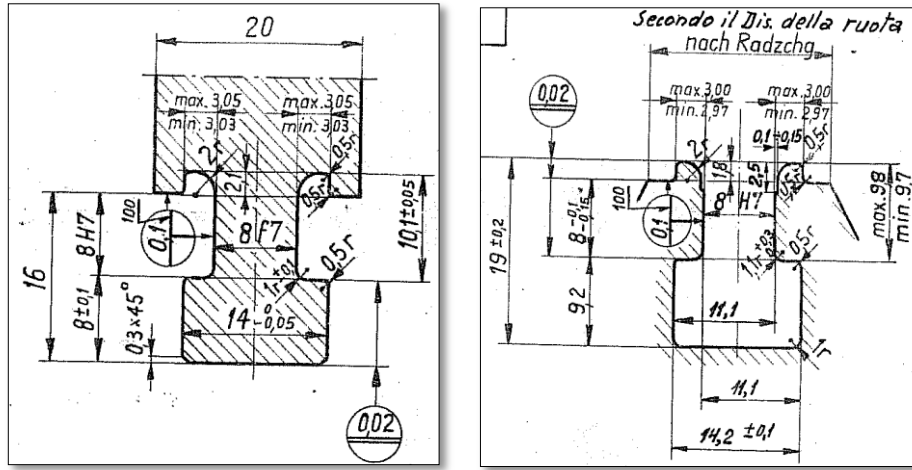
dimensioni del piede palare e della cava sul disco del 1° stadio della turbina n° 2.
